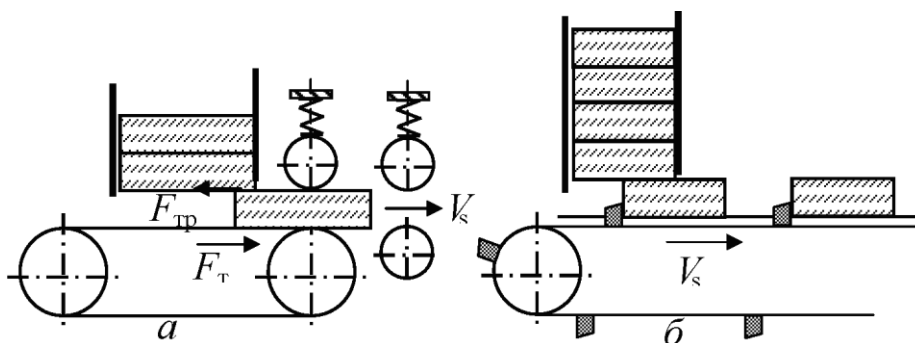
Магазинні живильники: а - стрічковий; б - ланцюговий з упорами
